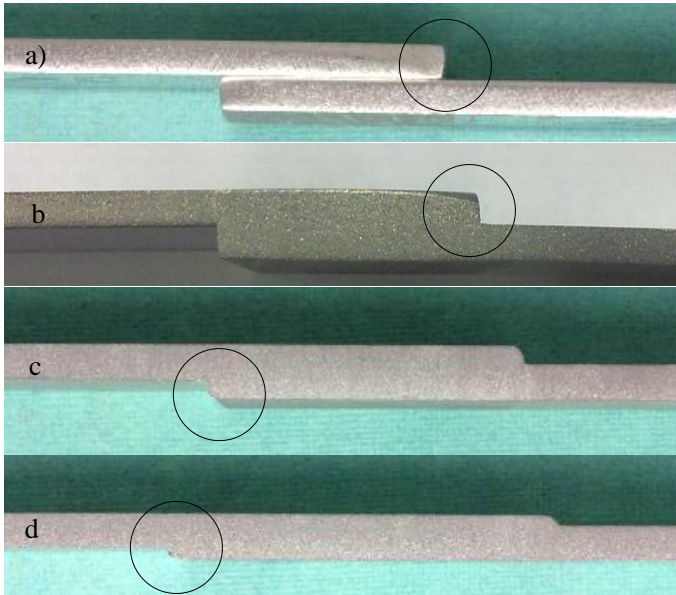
Vista lateral dos corpos de prova: a) AISI 316L soldado com 18 MPa, b) AISI 316L soldado com 35 MPa, c) super duplex UNS 32750 soldado com 30 MPa e d) duplex UNS 31803 soldado com 30 MPa.
